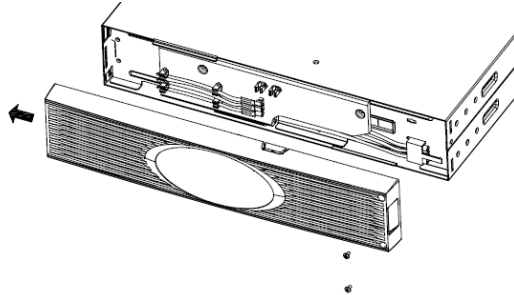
Entfernen der Frontblende vom Batteriepaket
